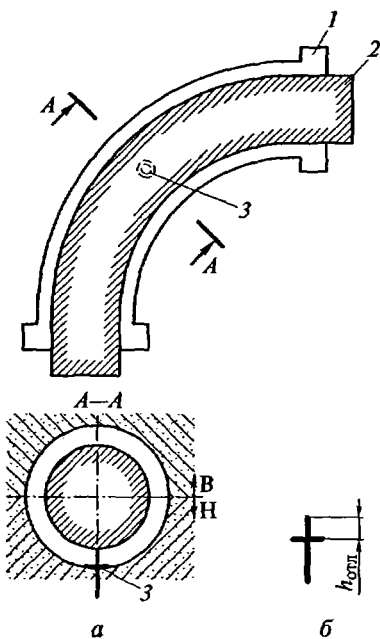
Фиксация стержня отливки патрубка жеробейкой:
